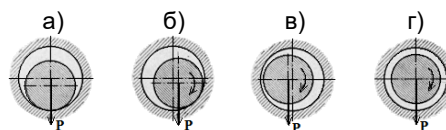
Варианты расположения цапфы вала в подшипнике скольжения
